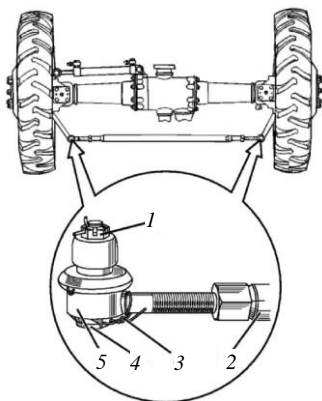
Проверка люфта в шарнирах рулевой тяги: 1 – корончатая гайка; 2 – рулевая тяга; 3 – контрольная проволока; 4 – резьбовая пробка; 5 – шарнир
